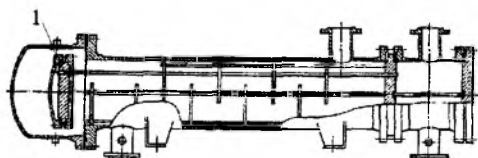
Теплообменник с плавающей головкой и разъемным опорным кольцом: 1 — плавающая головка
